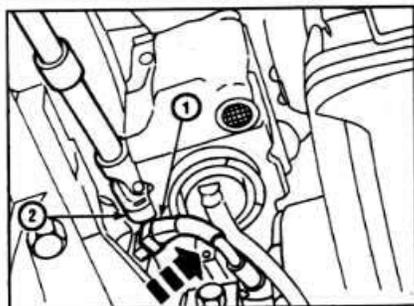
А.28. Расположение разъема датчика угла поворота коленчатого вала (1) и болта крепления корпуса фильтра системы пульсации воздуха (2).
